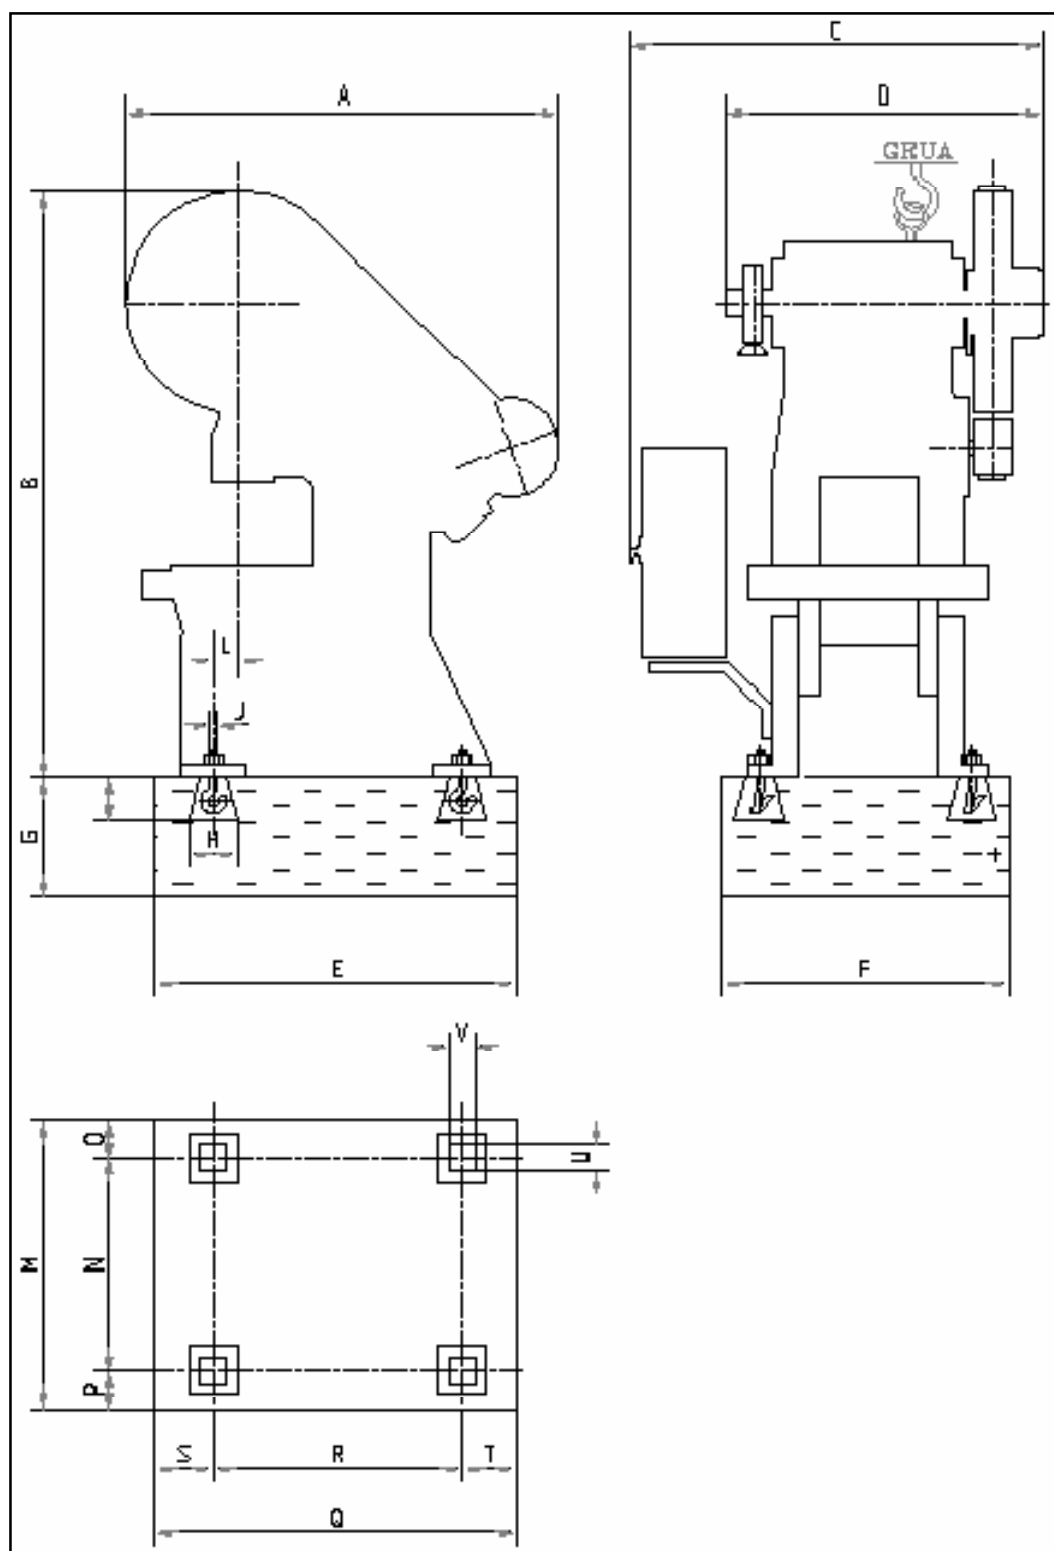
Dimensões gerais e das fundações da prensa [15]
